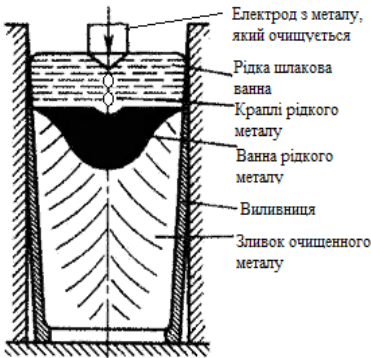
Схема електрошлакового переплавлення металу
